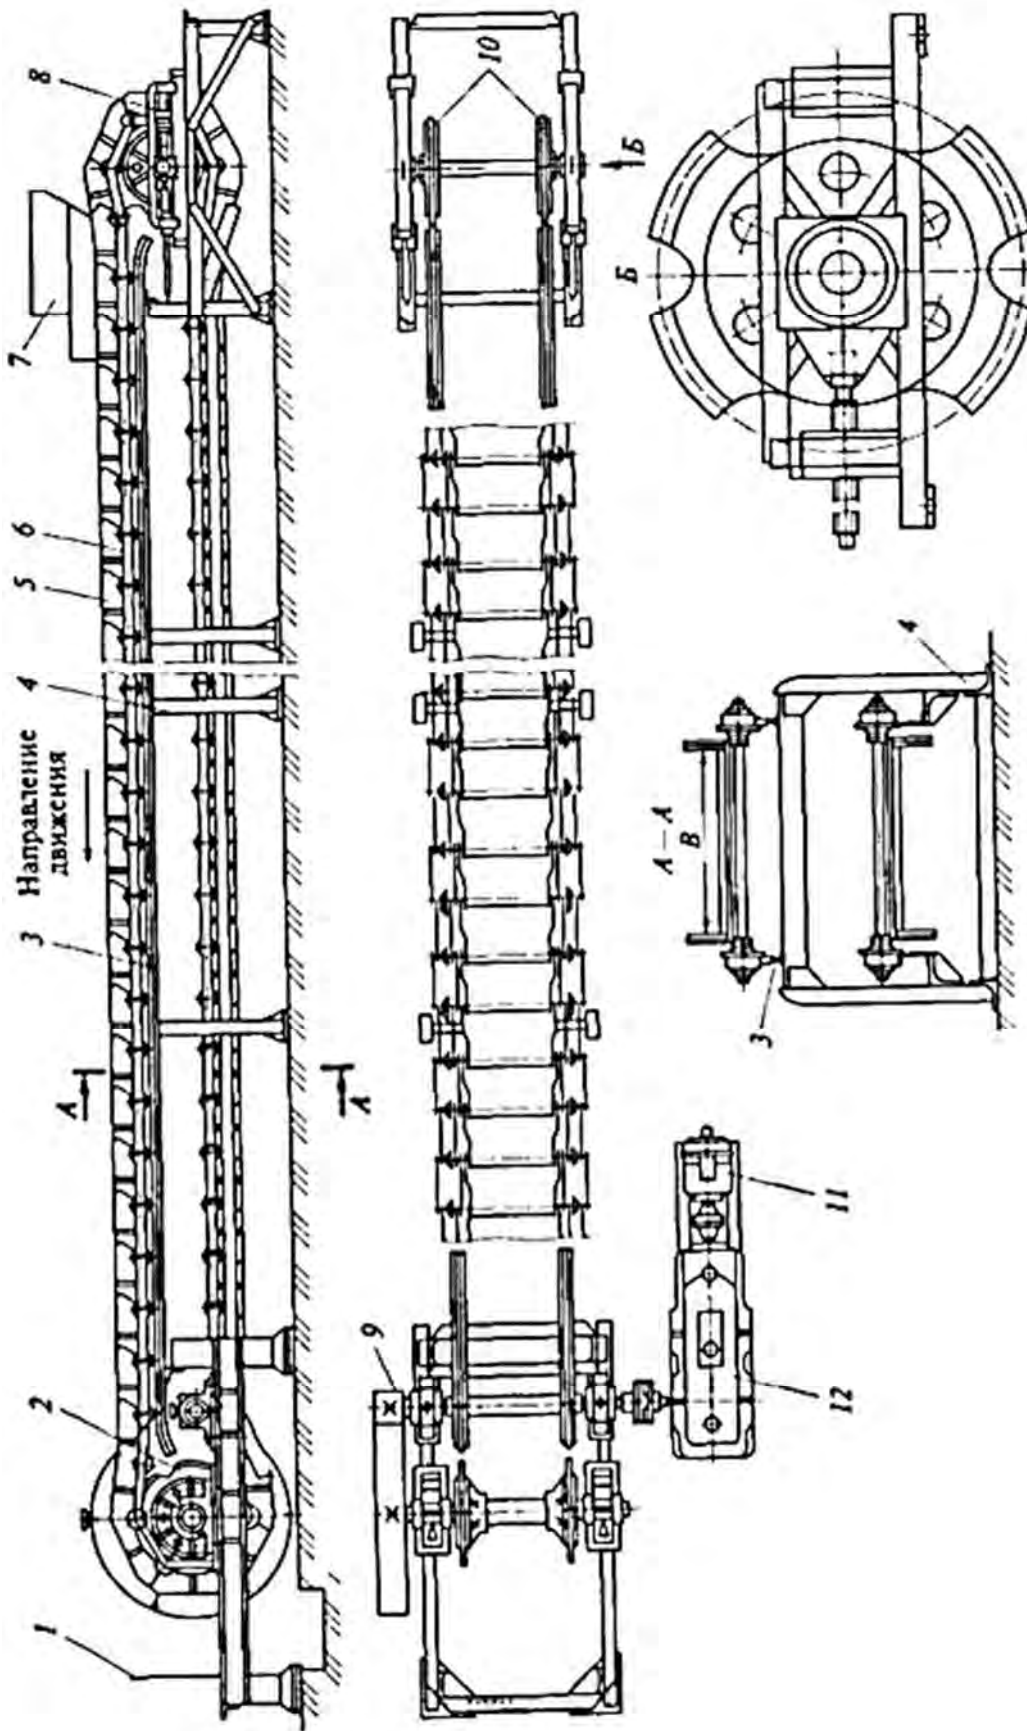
Пластинчатый конвейер: 1, 7 – разгрузочная и загрузочная воронки; 2 – приводная звездочка; 3 – направляющая; 4 – рама; 5 – бортовой настил; 6 – катковая цепь; 8 – натяжная цепь; 9 – натяжное устройство; 10 – зубчатая передача; 11 – электродвигатель; 12 – редуктор;  $B$  – ширина настила
